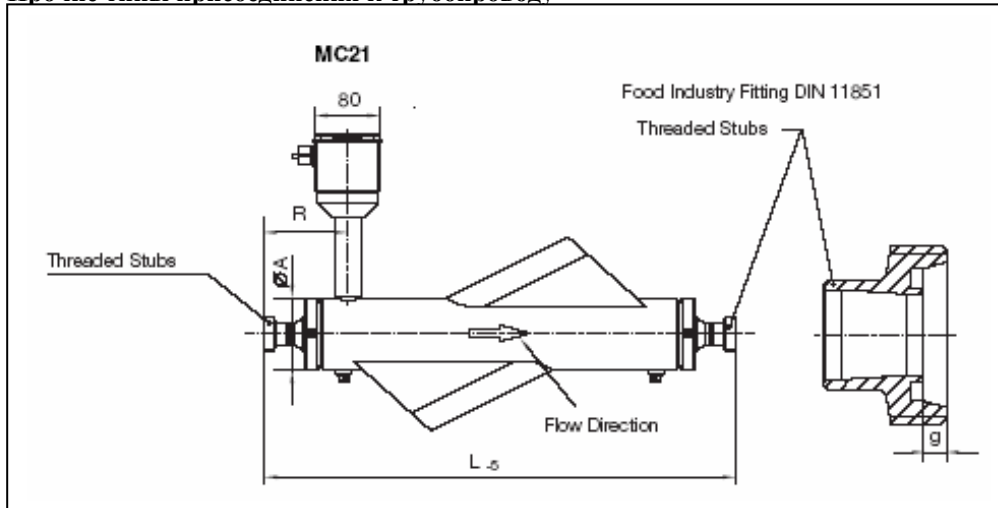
/27 Молочная гайка (Food Industry Fitting размеры „D“ to „F“, DIN 11851)
